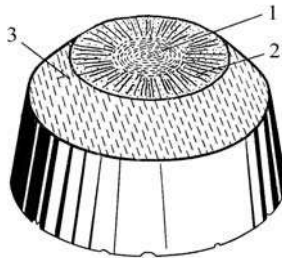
Схема зламу, який утворився після розтягнення гладкого циліндричного зразка
